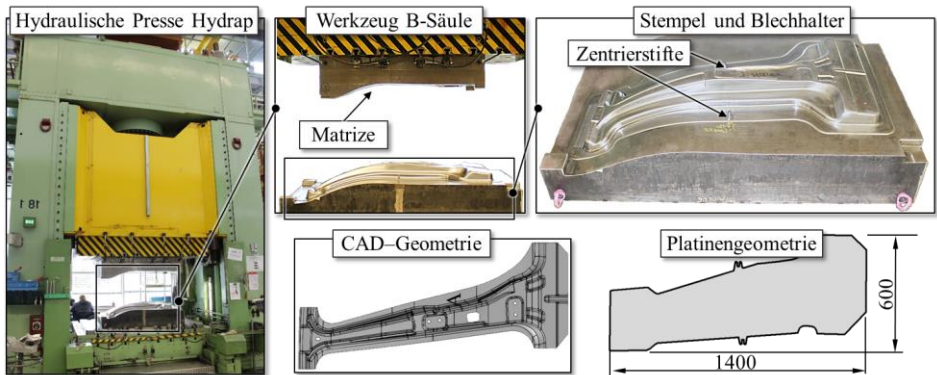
Versuchsaufbau B-Säule mit Presse, Werkzeug, CAD-Geometrie und Platinenzuschnitt
